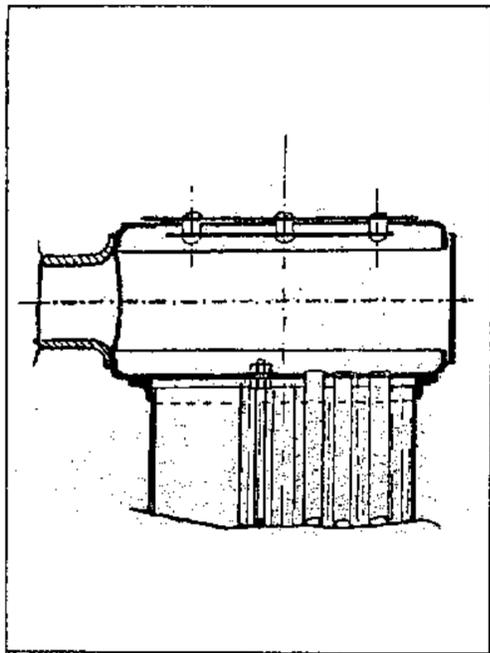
/2: Verbindung der Rauchkammer mit dem Zylinderkessel (Ausführungsbeispiel)
